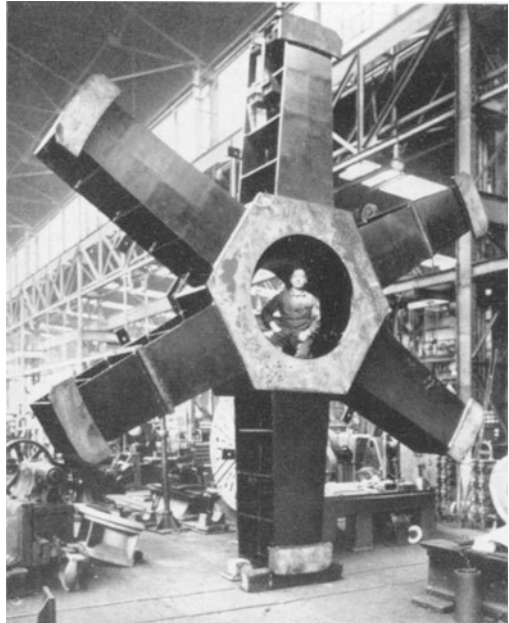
Geschweißter Läufer einer Dynamo.
